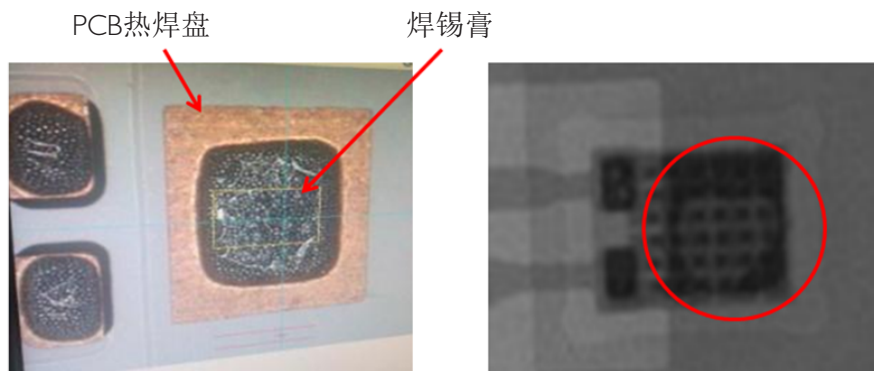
一块尺寸太小的网板开口会产生负面效应，导致焊膏在回流前喷涂至热焊盘及电极焊盘是失效的，回流后焊膏的覆盖状况糟糕。
